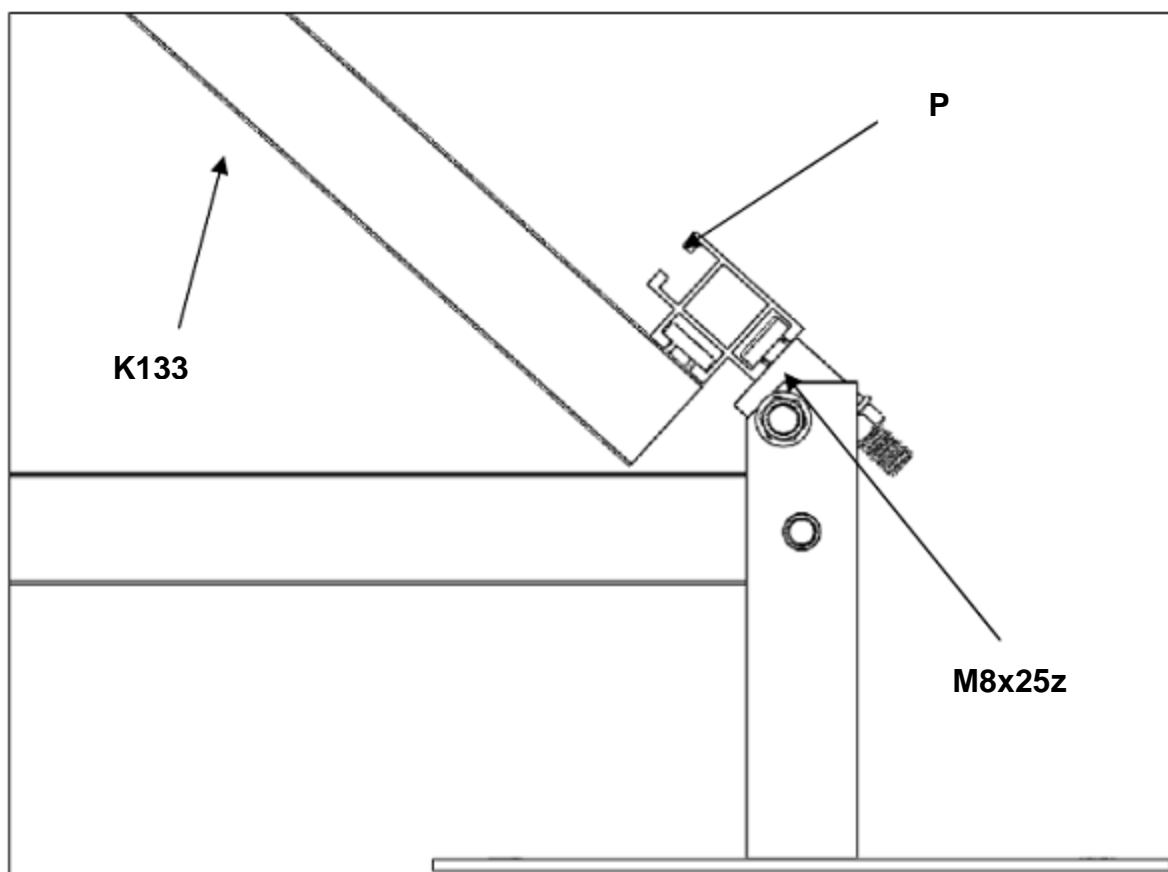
/ Obr. č. 6/ Rys. 6/ Fig. no. 6
